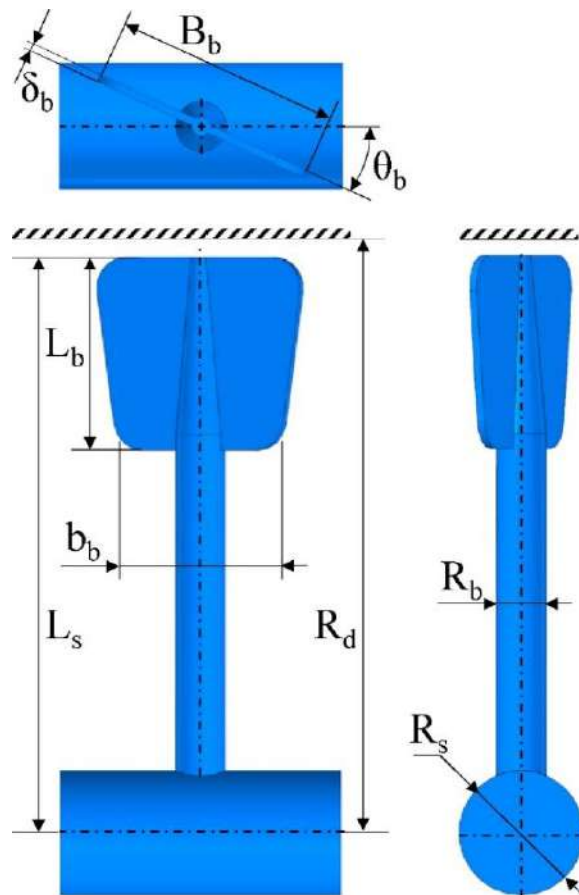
Конструктивна схема лопаті лопатевого валу змішувача:
